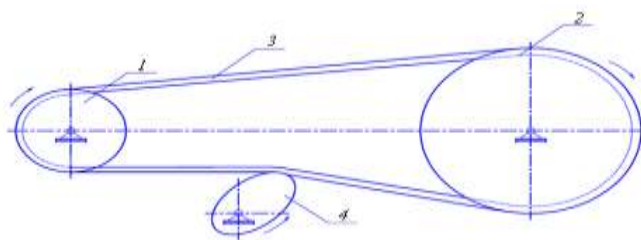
Схема ременной передачи с натяжным профилем кулачка
